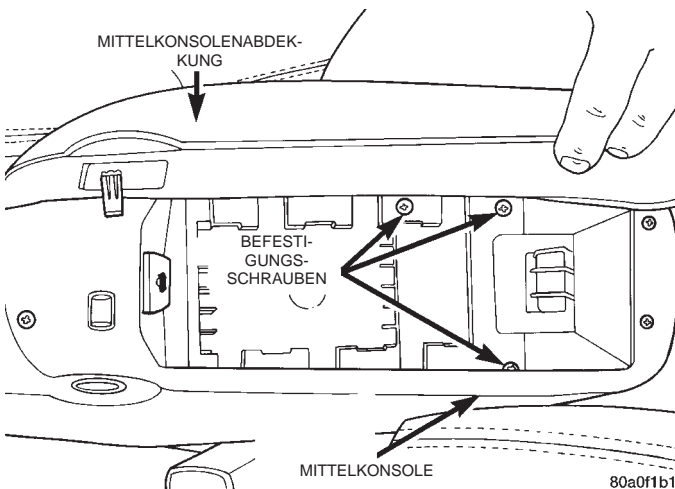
Befestigungsschrauben am hinteren Teil der Mittelkonsole
